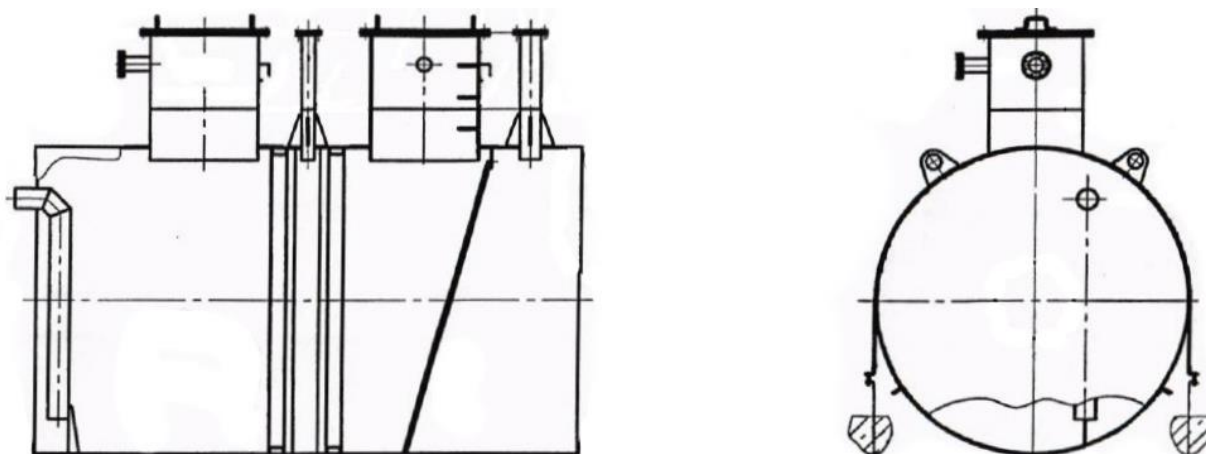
Общий вид эскиза резервуара РГС-40
